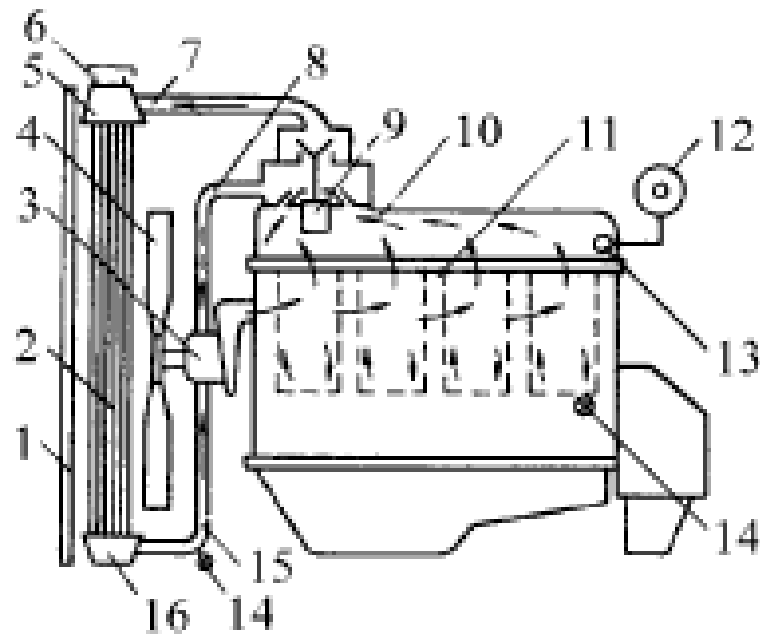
Схема жидкостной системы охлаждения: 1 – жалюзи; 2 – сердцевина радиатора; 3 – водяной насос; 4 – вентилятор; 5 – верхний бачок радиатора; 6 – пробка радиатора с паровоздушным клапаном; 7 – верхний патрубок; 8 – перепускной патрубок; 9 – термостат; 10 – водяная рубашка головки; 11 – водяная рубашка блока цилиндров; 12 – термометр; 13 – датчик термометра; 14 – сливной кран; 15 – нижний патрубок; 16 – нижний бачок радиатора
